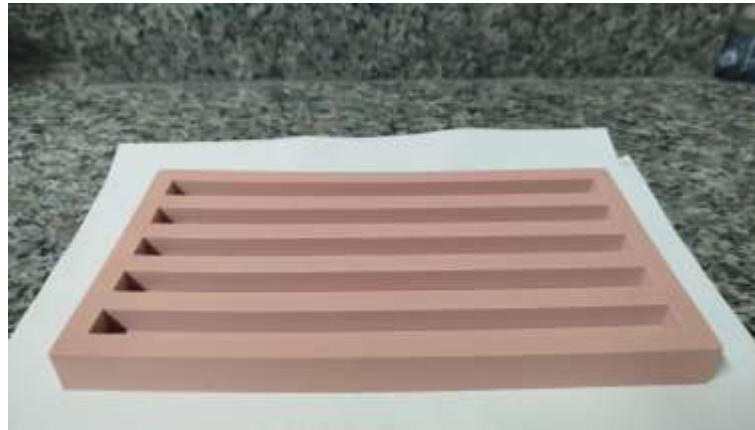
Molde de silicone produzido para fabricação dos corpos de prova. Fonte: Autor (2026)
